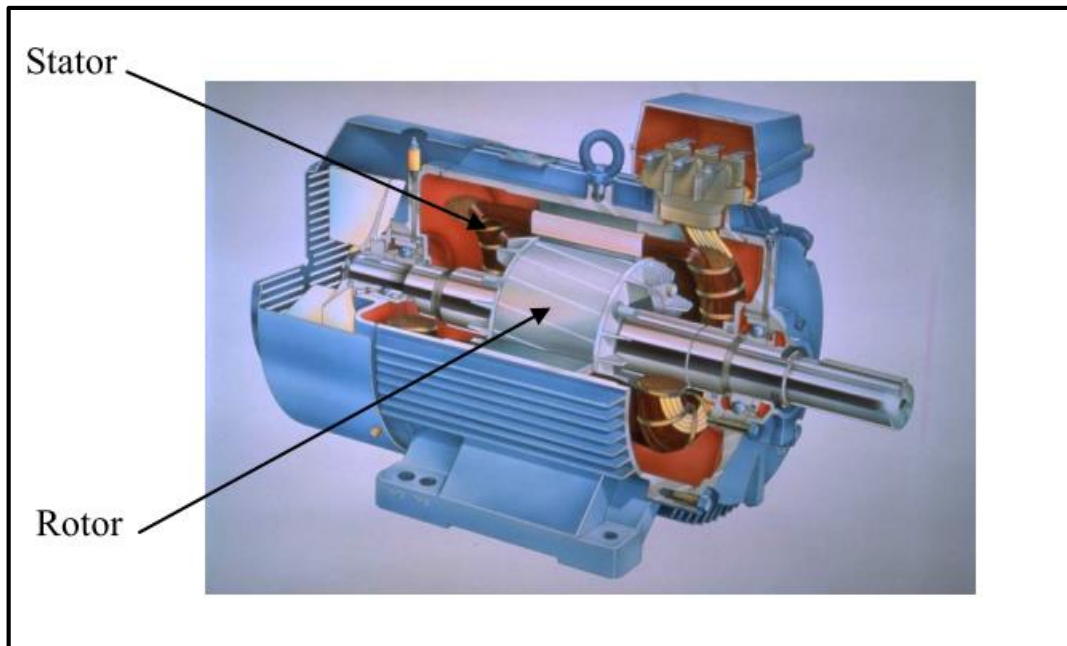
Structure de la machine asynchrone triphasée à cage.
